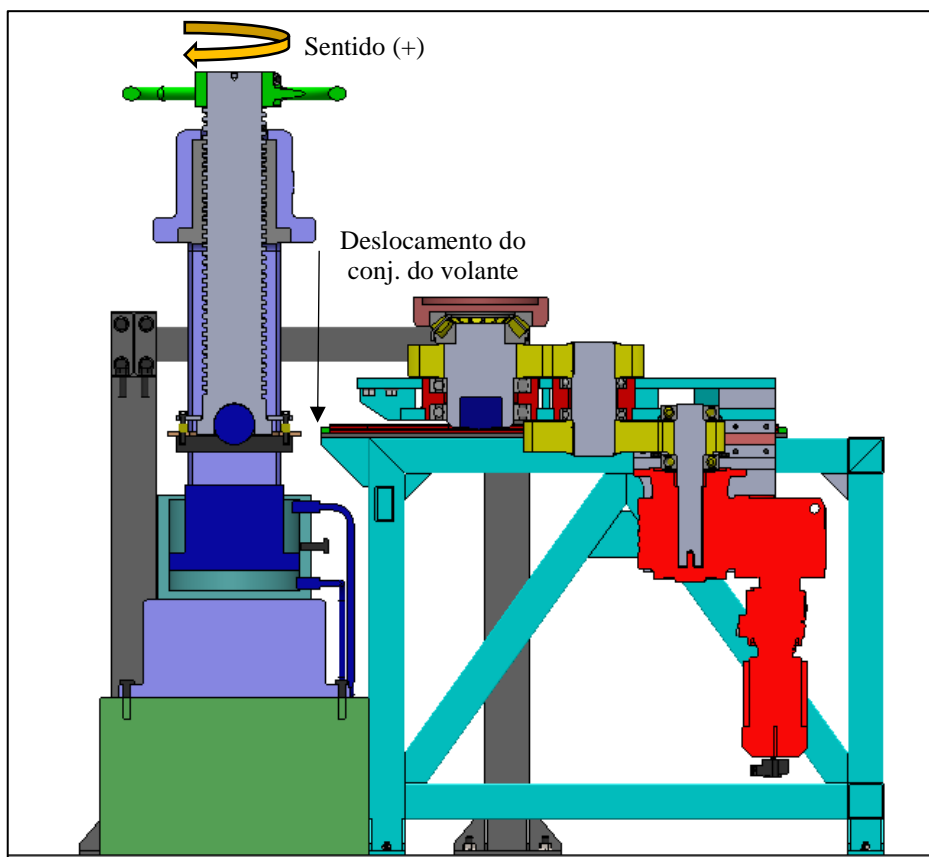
Representação esquemática em vista de seção de corte transversal destacando os componentes instalados e a distância deslocada do conjunto do volante da máquina de compressão
